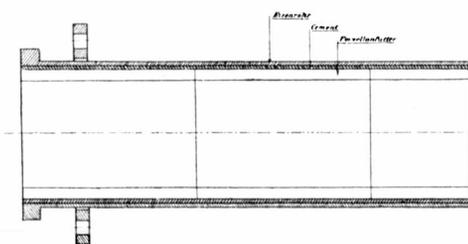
Spülversatzrohr mit Porzellanfutter.
